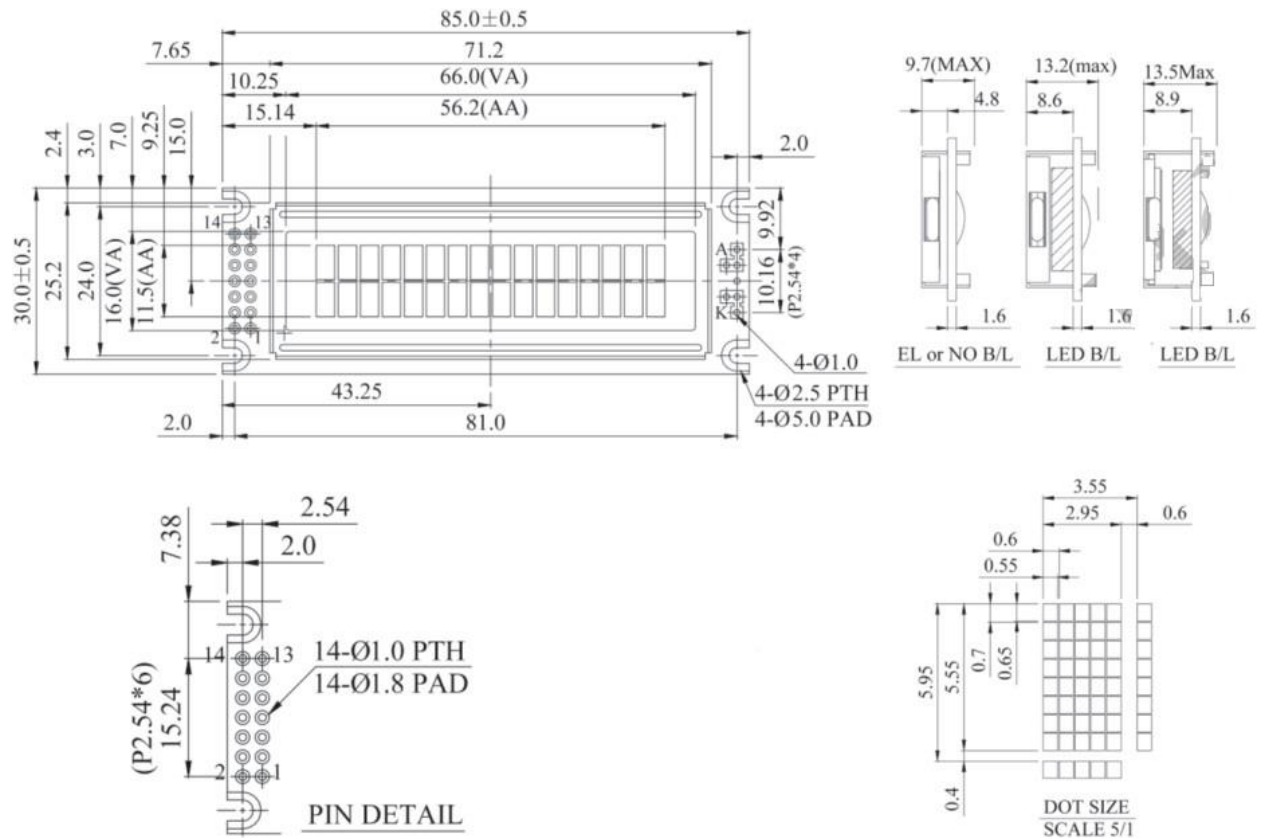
Зовнішній вигляд і розміри корпусу LCD-дисплея WH1602D-PGH-CT [12]
